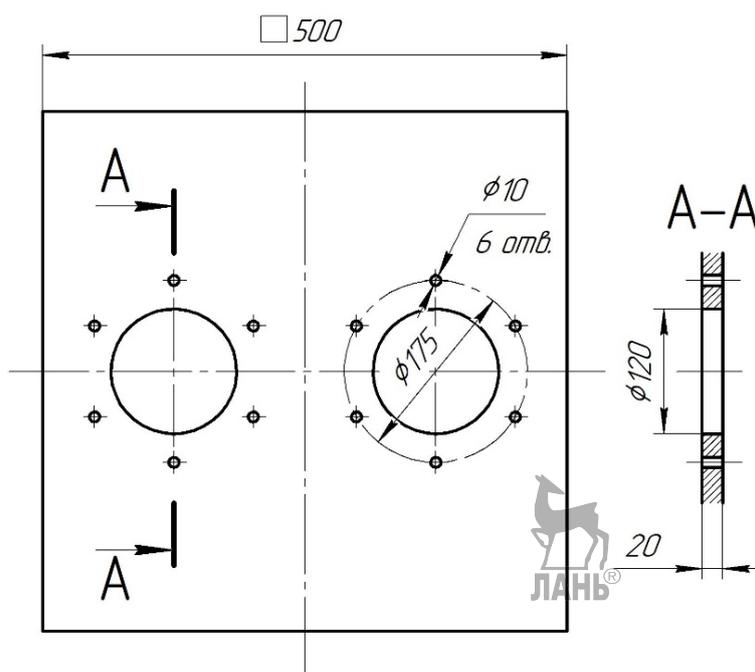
Чертеж передней пластины корпуса ОПУ
